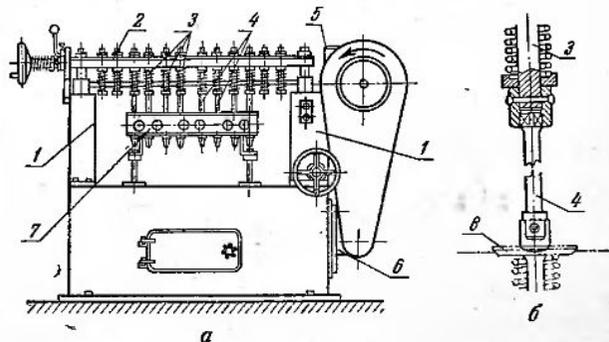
Станок для притирки клапанов автотракторных двигателей: 1 — стойки; 2 — корпус шпинделей; 3 — шпиндели; 4 — штуцера; 5 — редуктор; 6 — электродвигатель; 7 — головка цилиндров; 8 — клапан.
